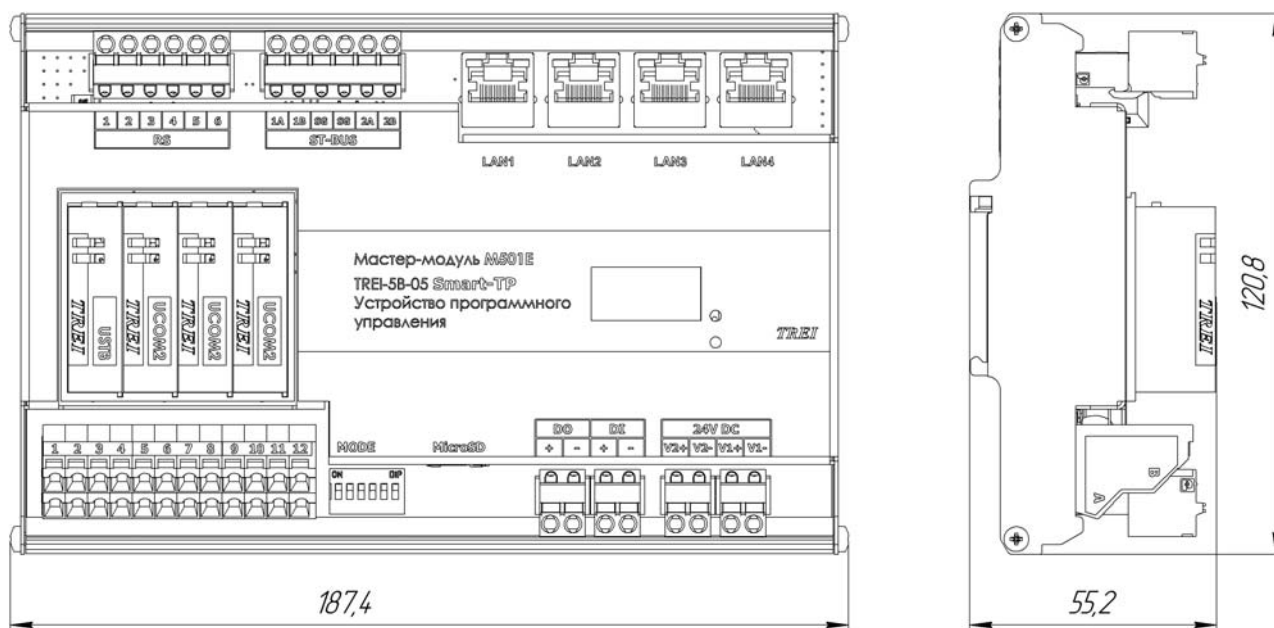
Чертеж общего вида M501E с указанием габаритных и присоединительных размеров
